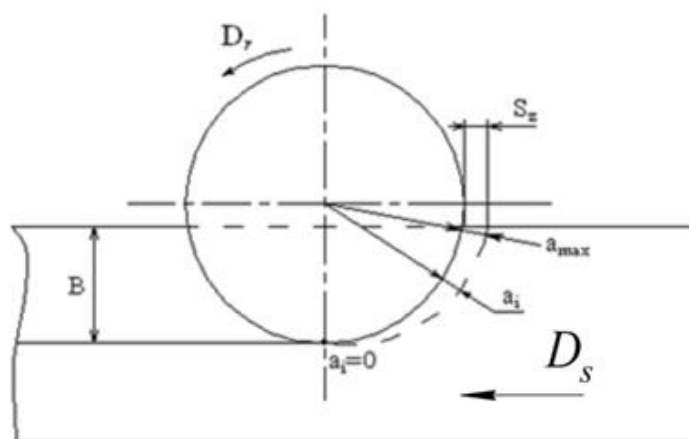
Схема торцевого несимметричного неполного фрезерования (вид сверху)
